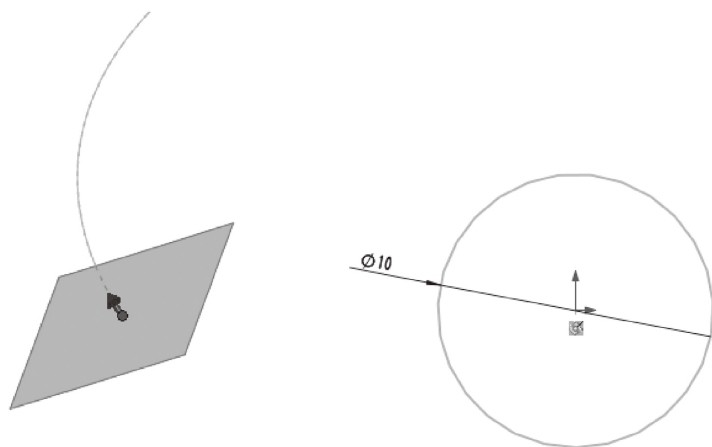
绘制螺旋线断面圆草图并标注尺寸
